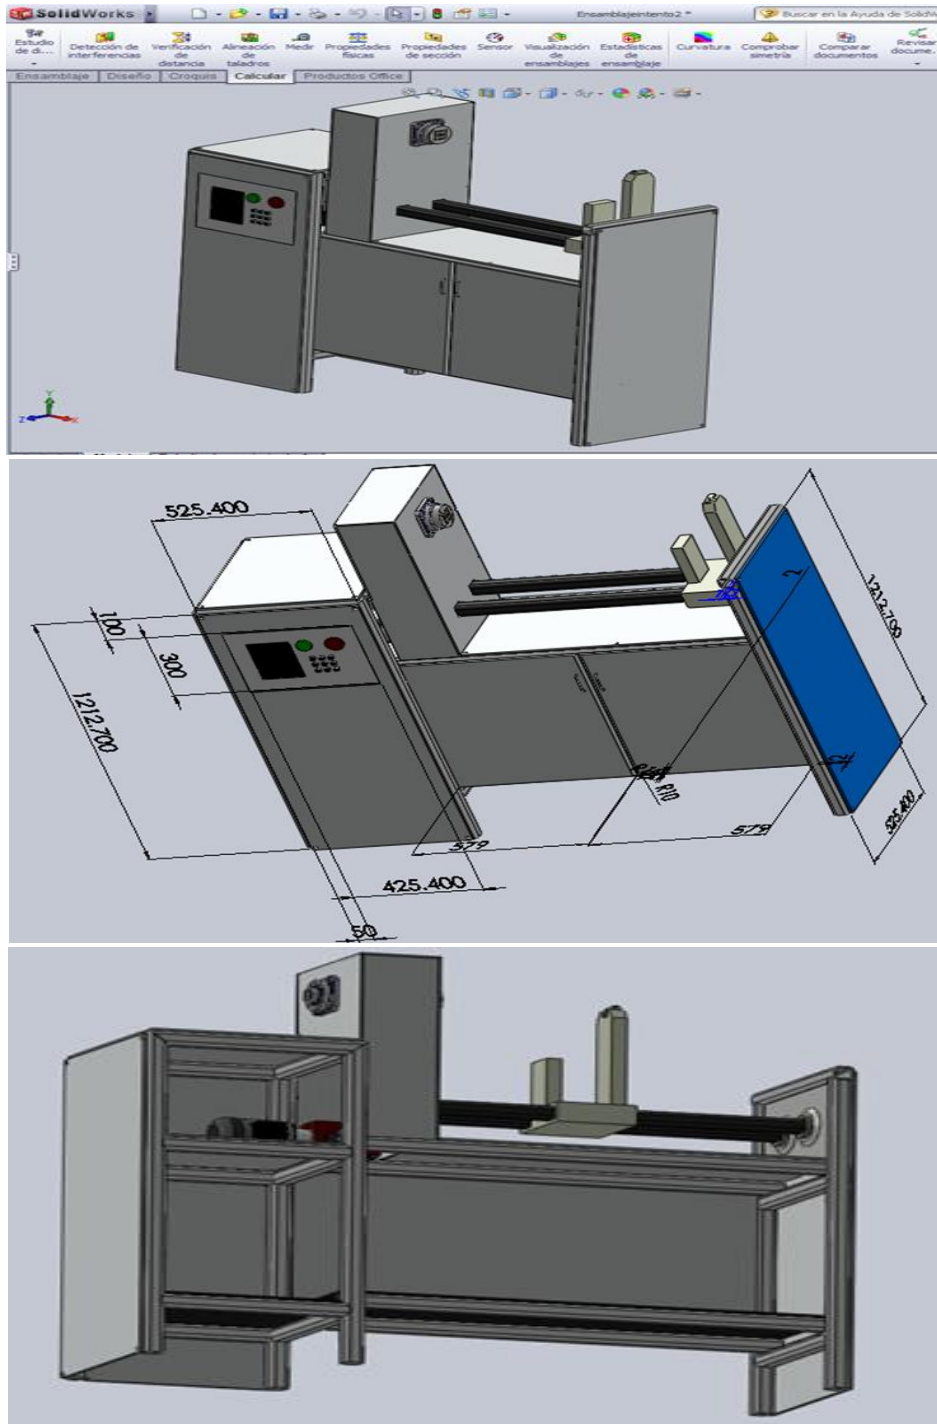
Diseño en Solidworks® de la maquina torsionadora Fuente: Autor
